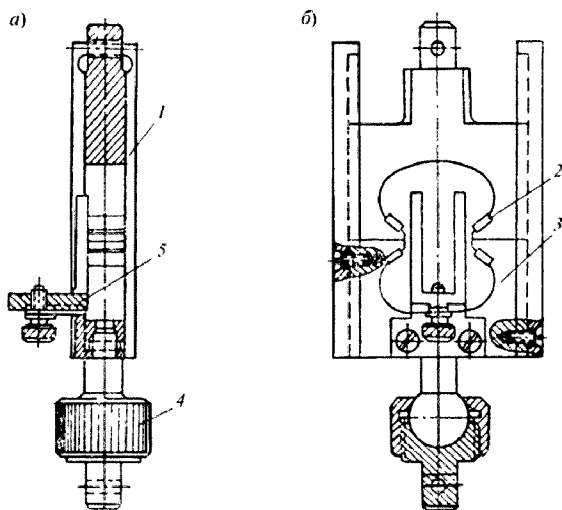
Приспособление для испытания образцов, имеющих форму восьмерок, на разрыв:
